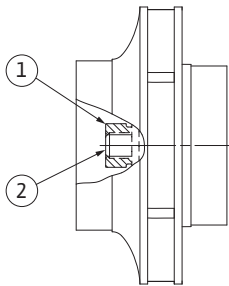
Poziția corectă a piuliței rotorului după montaj
